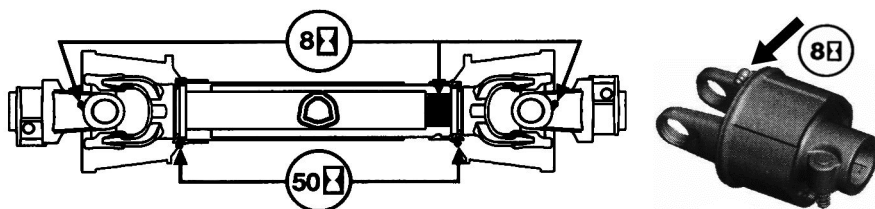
Смазка карданного вала и храповой муфты
